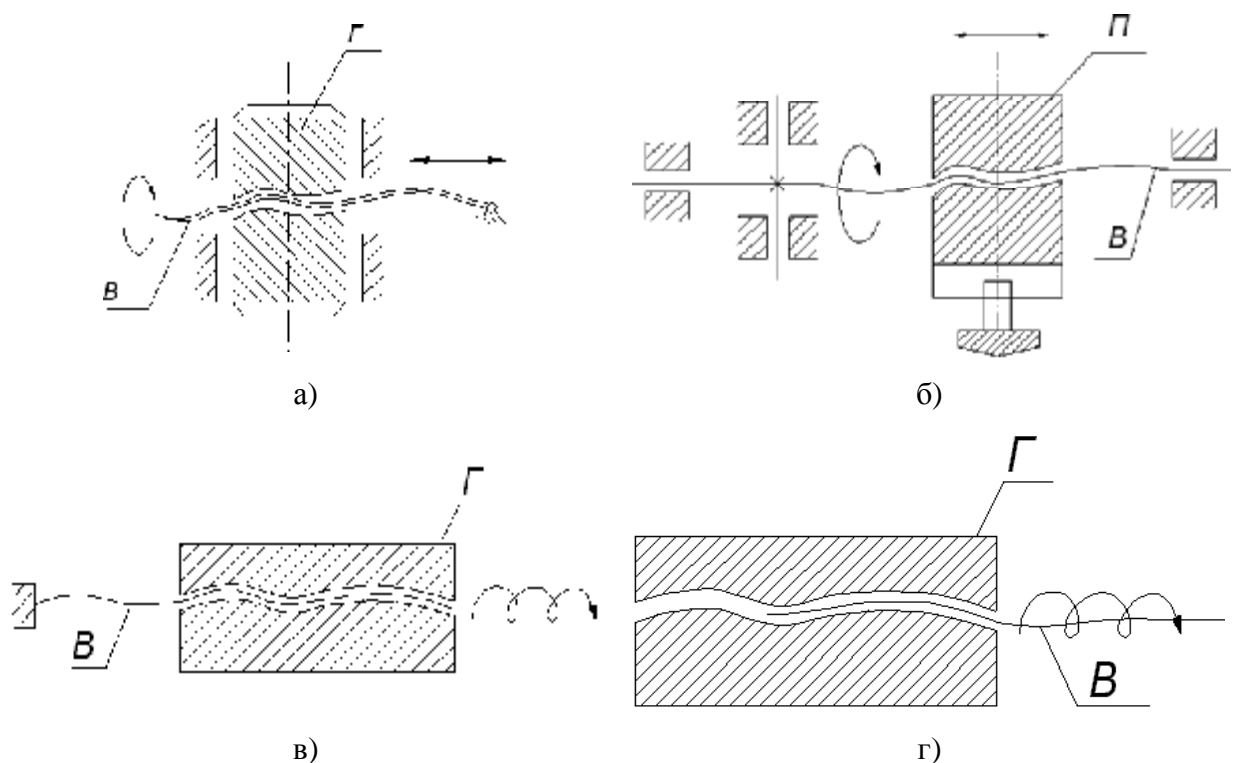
Гвинтові механізми: а – обертання гайки перетворюється в поступальний рух
